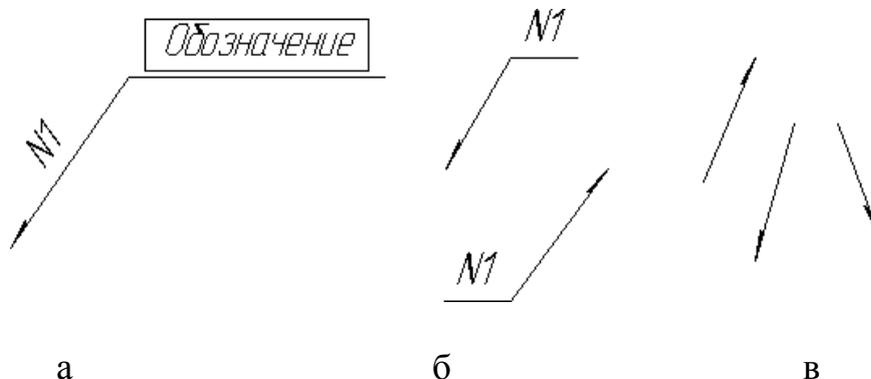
Образец выполнения упрощений обозначений швов сварных соединений.
